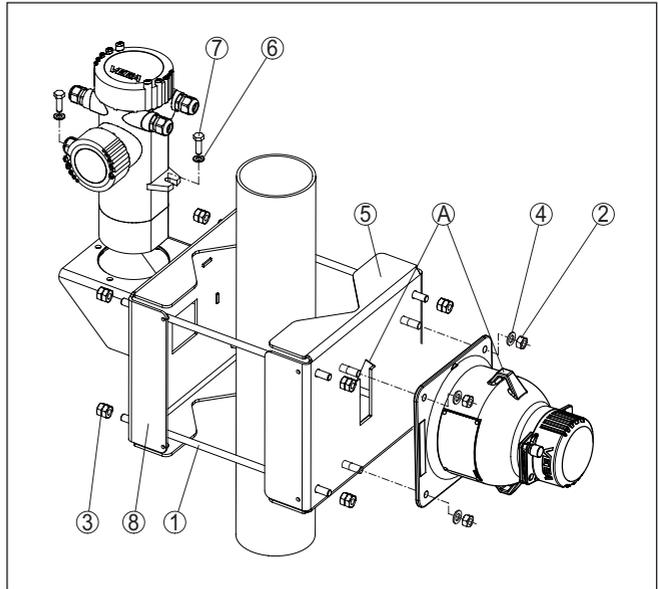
Dispositivo de fixação com sensor montado na vertical (com VEGA-SOURCE 81, 82, 83)
